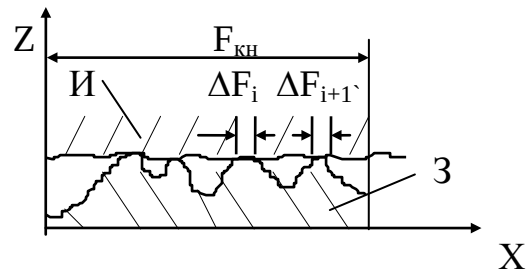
Схема контакта заготовки и инструмента при сухом трении
